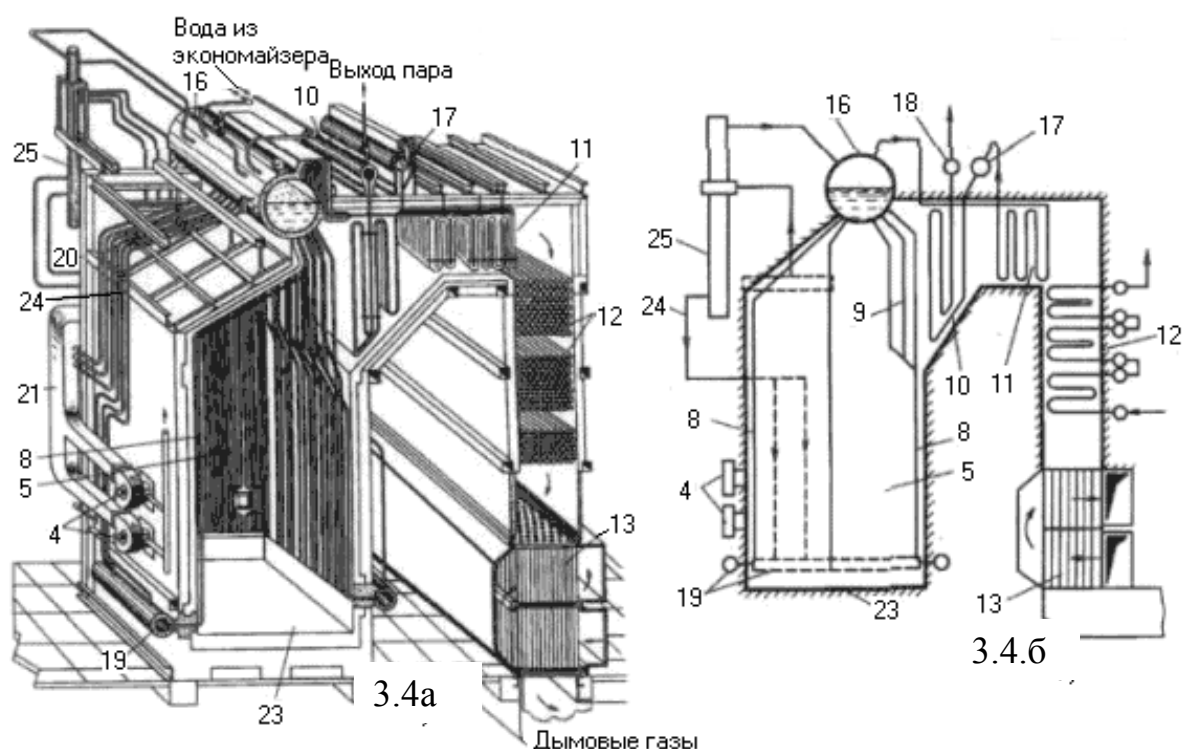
а, б – Конструктивное выполнение и схемы барабанных паровых котлов: а - для сжигания газа и мазута; б - то же, схема котла; 1 - топливный бункер (бункер сырого топлива); 2 - скребковый питатель мельницы; 3 - углеразмольная мельница с сепарационной шахтой; 4 - горелка; 5 - топочная камера; 6 - холодная воронка для удаления шлака; 7 - шлакоприемная ванна; 8 - настенные трубные экраны; 9 - многорядный пучок труб (фестон); 10, 11 - вторая и первая ступени конвективного пароперегревателя; 12, 14 - то же конвективного экономайзера; 13, 15 - то же воздухоподогревателя; 16 - барабан; 17 - регулятор перегрева пара; 18 - выходная камера пароперегревателя; 19 - нижний коллектор топочного экрана; 20 - каркас котла; 21 - короб подвода горячего воздуха; 22 - обмуровка котла; 23 - горизонтальный под топки; 24 - опускные трубы; 25 - выносной циклон-сепаратор.
